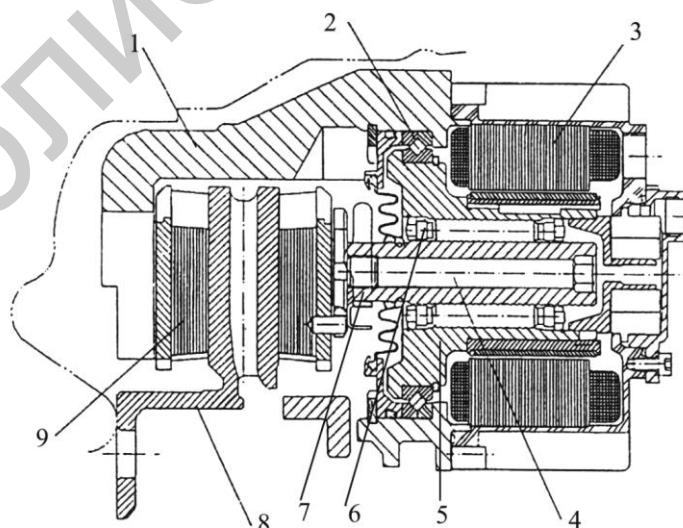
Тормозной механизм электромеханической тормозной системы: 1 – кулак; 2 – подшипник; 3 – статор; 4 – ходовой винт (шпиндель); 5 – ротор; 6 – сателлитная шестерня; 7 – солнечная шестерня; 8 – тормозной диск; 9 – тормозная колодка
